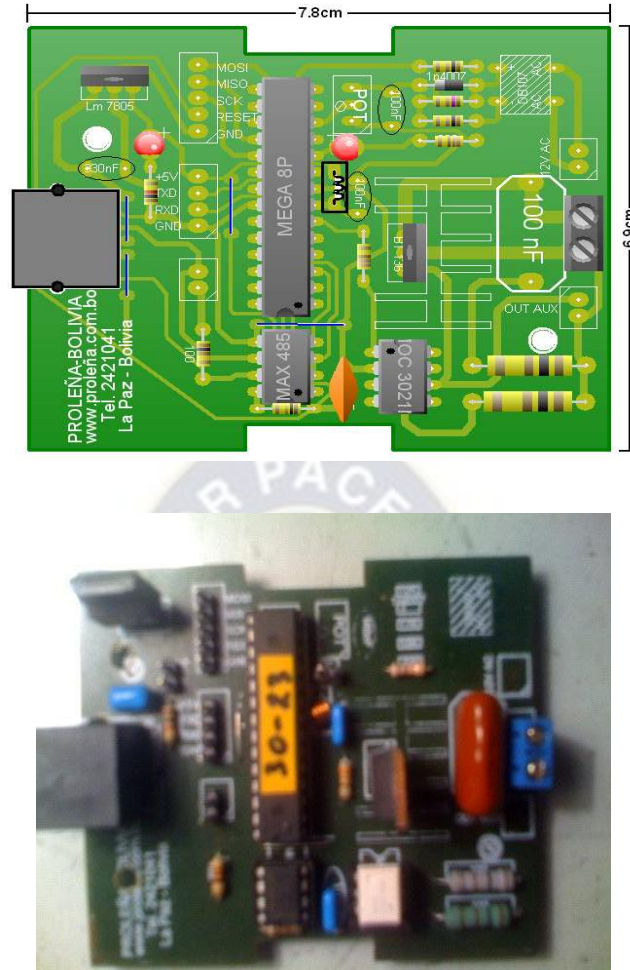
CIRCUITO PCB FINAL PERIFÉRICO RMS/AC
